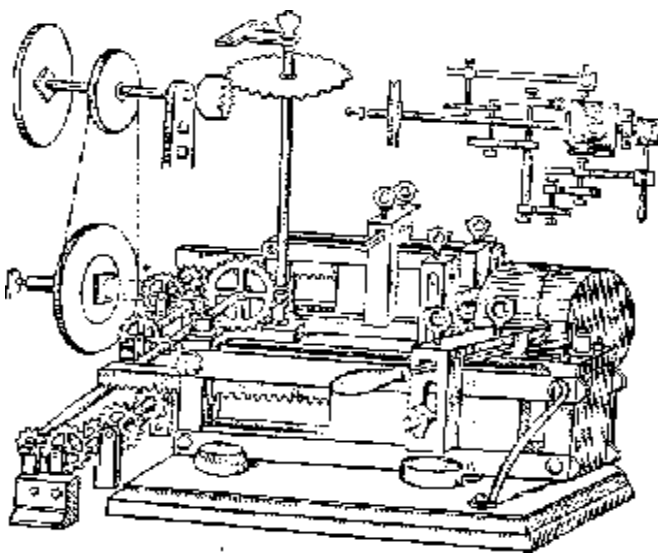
Кінематична схема токарно-копіювального верстата А. К. Нартова, 1712 н.
